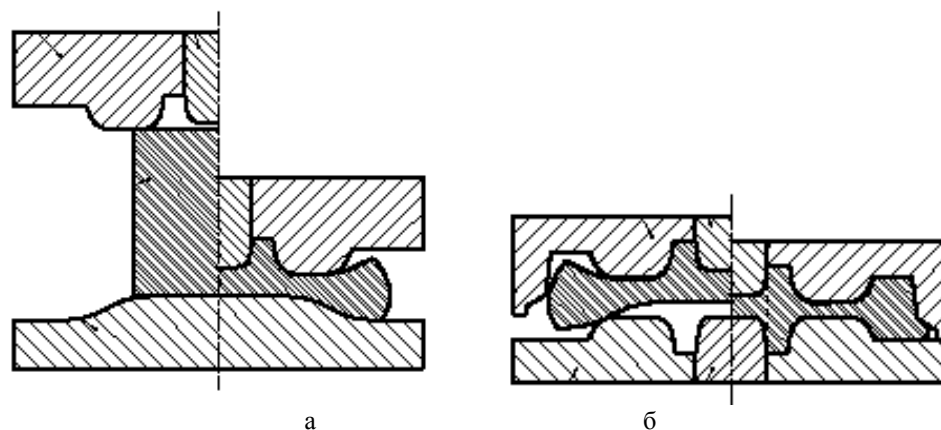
Схема черновой (а) и чистовой (б) штамповки по способу «SMS - EUMUCO»
